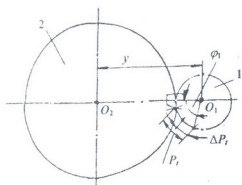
Схема нарезания некруглого цилиндрического колеса с наружными зубьями
